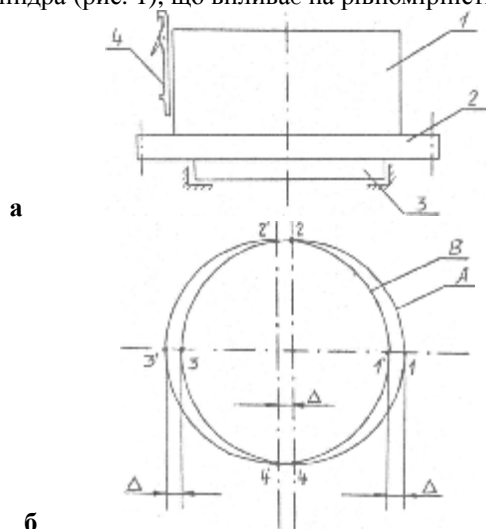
Опора голкового циліндра круглов'язальної машини типу КО: а – схема опори (1 – голковий циліндр; 2 – зубчасте колесо; 3 – опорна частина циліндра; 4 – голки); б – траєкторія руху голок (вигляд зверху): А – в початковий період роботи; В – при зношенні опори
